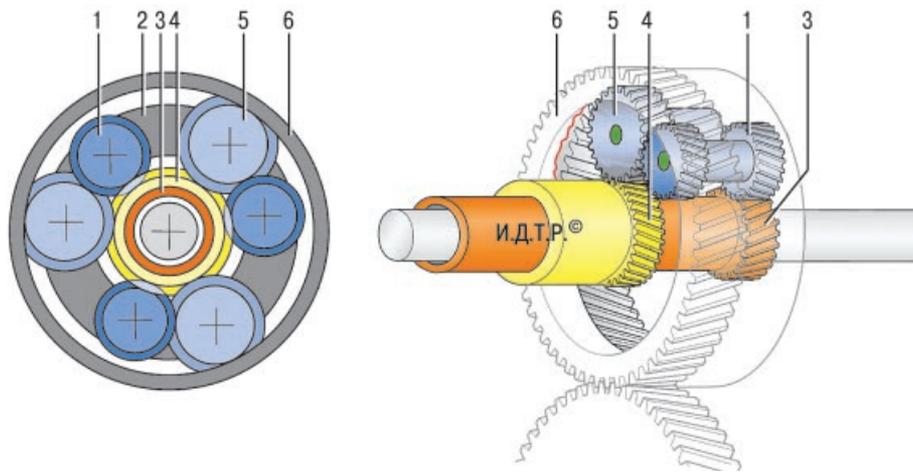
Планетарный редуктор системы Равинье: 1 – длинный сателлит; 2 – водило; 3 – малая солнечная шестерня; 4 – большая солнечная шестерня; 5 – короткий сателлит; 6 – коронная шестерня
